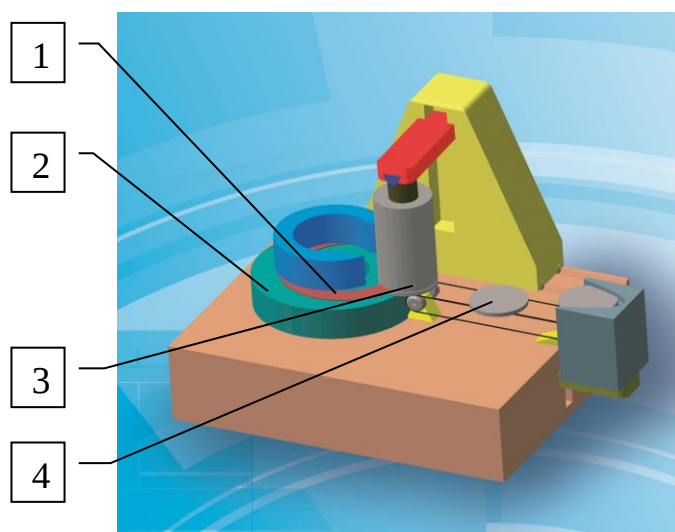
Резка монокристаллов на проход свободным кольцевым ротором в бесшпиндельном станке резки
